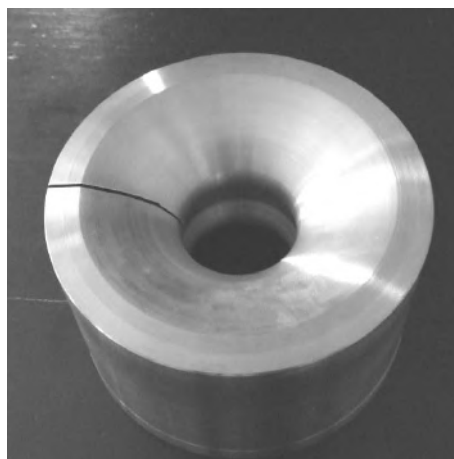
Массивный одновитковый соленоид рассчитанной формы
